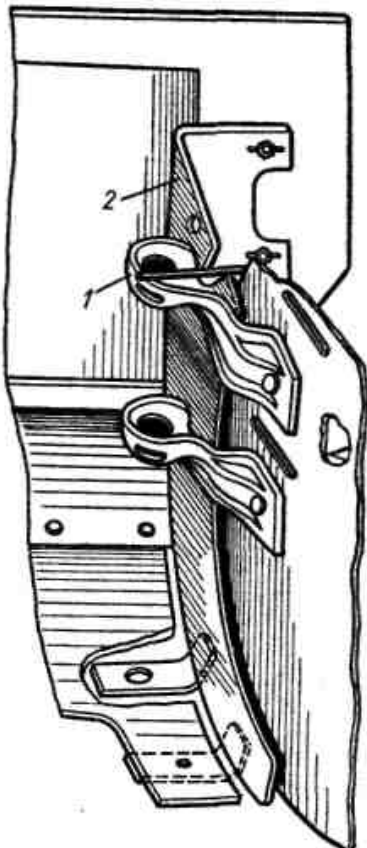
Регулювання положення боковий картоплесаджалок
